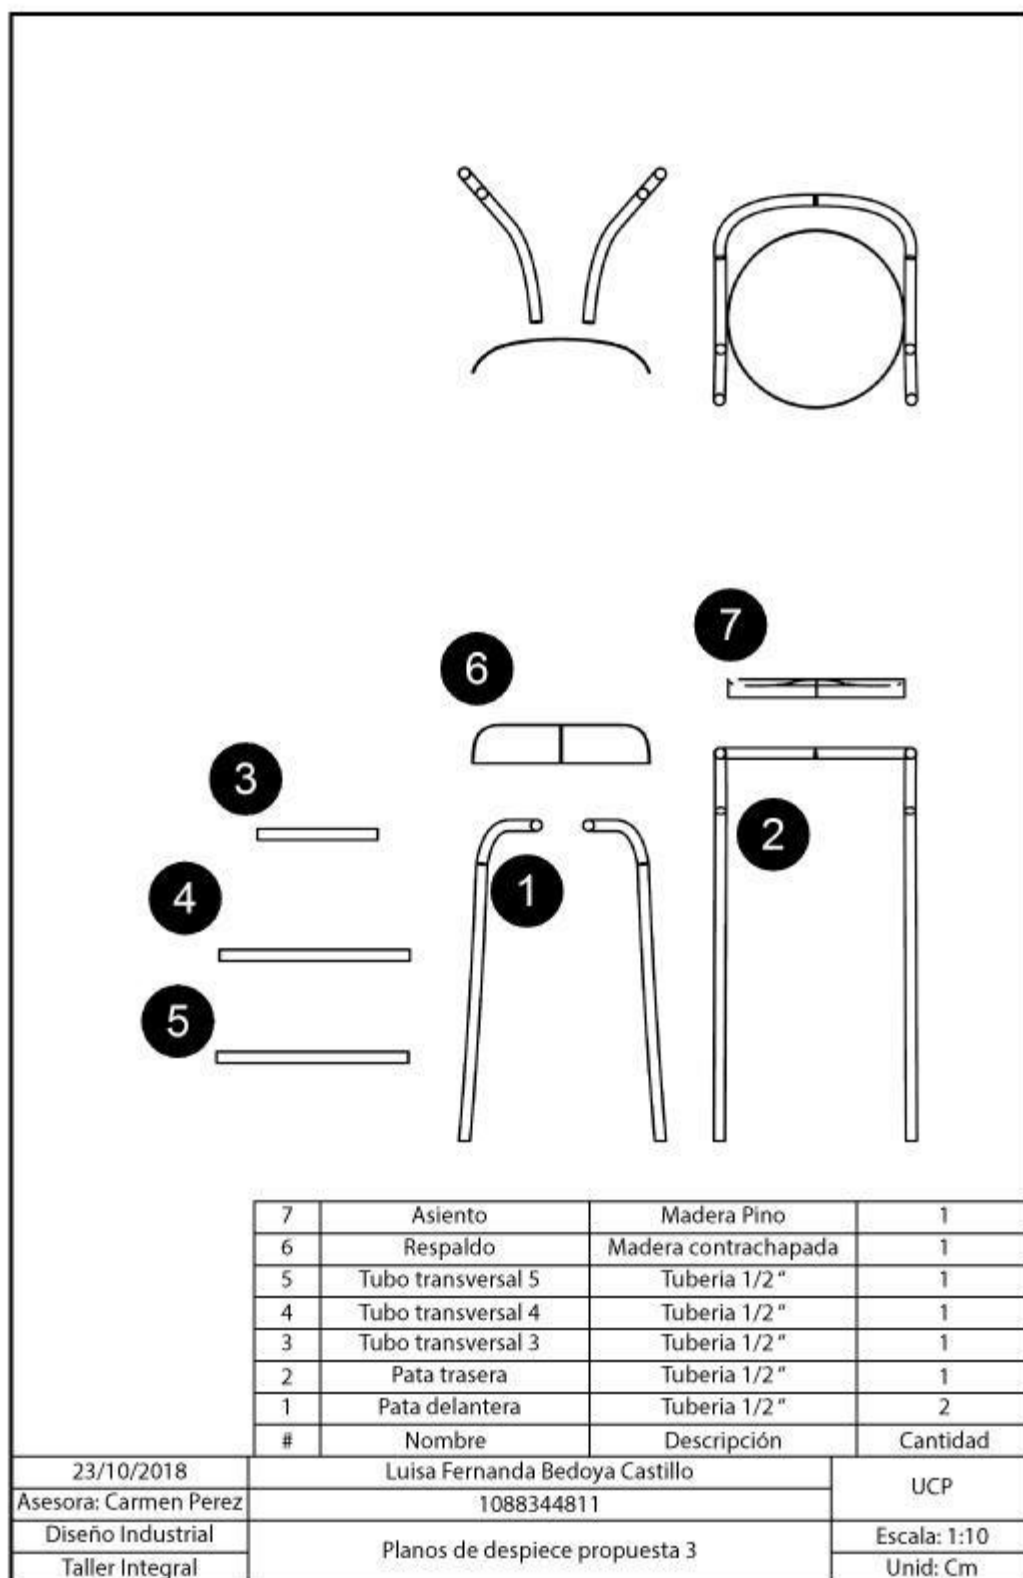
Planos de despiece propuesta 3. Fuente: Propia.
